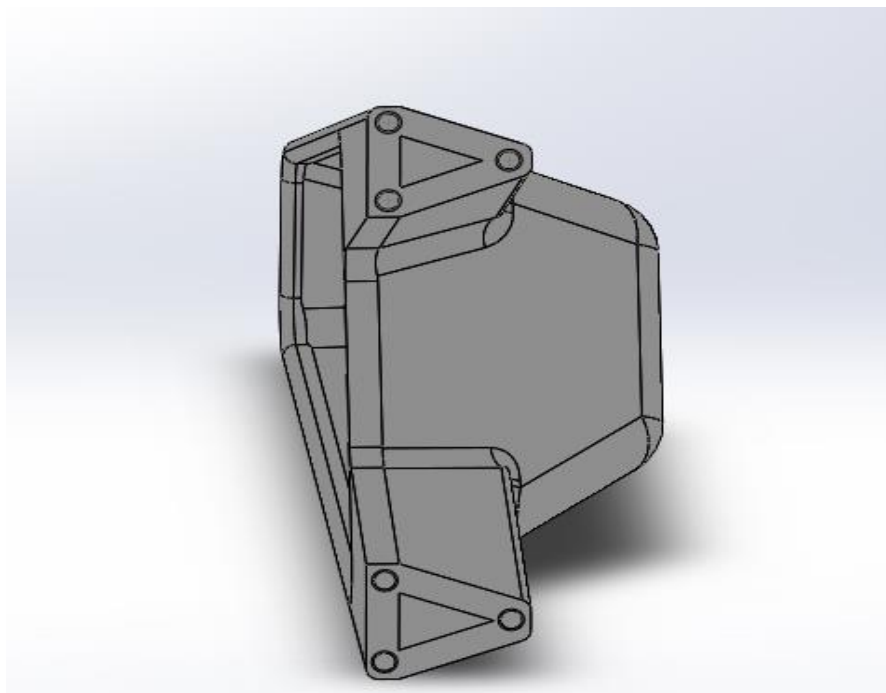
Disposición geométrica de los tornillos de los anclajes.
